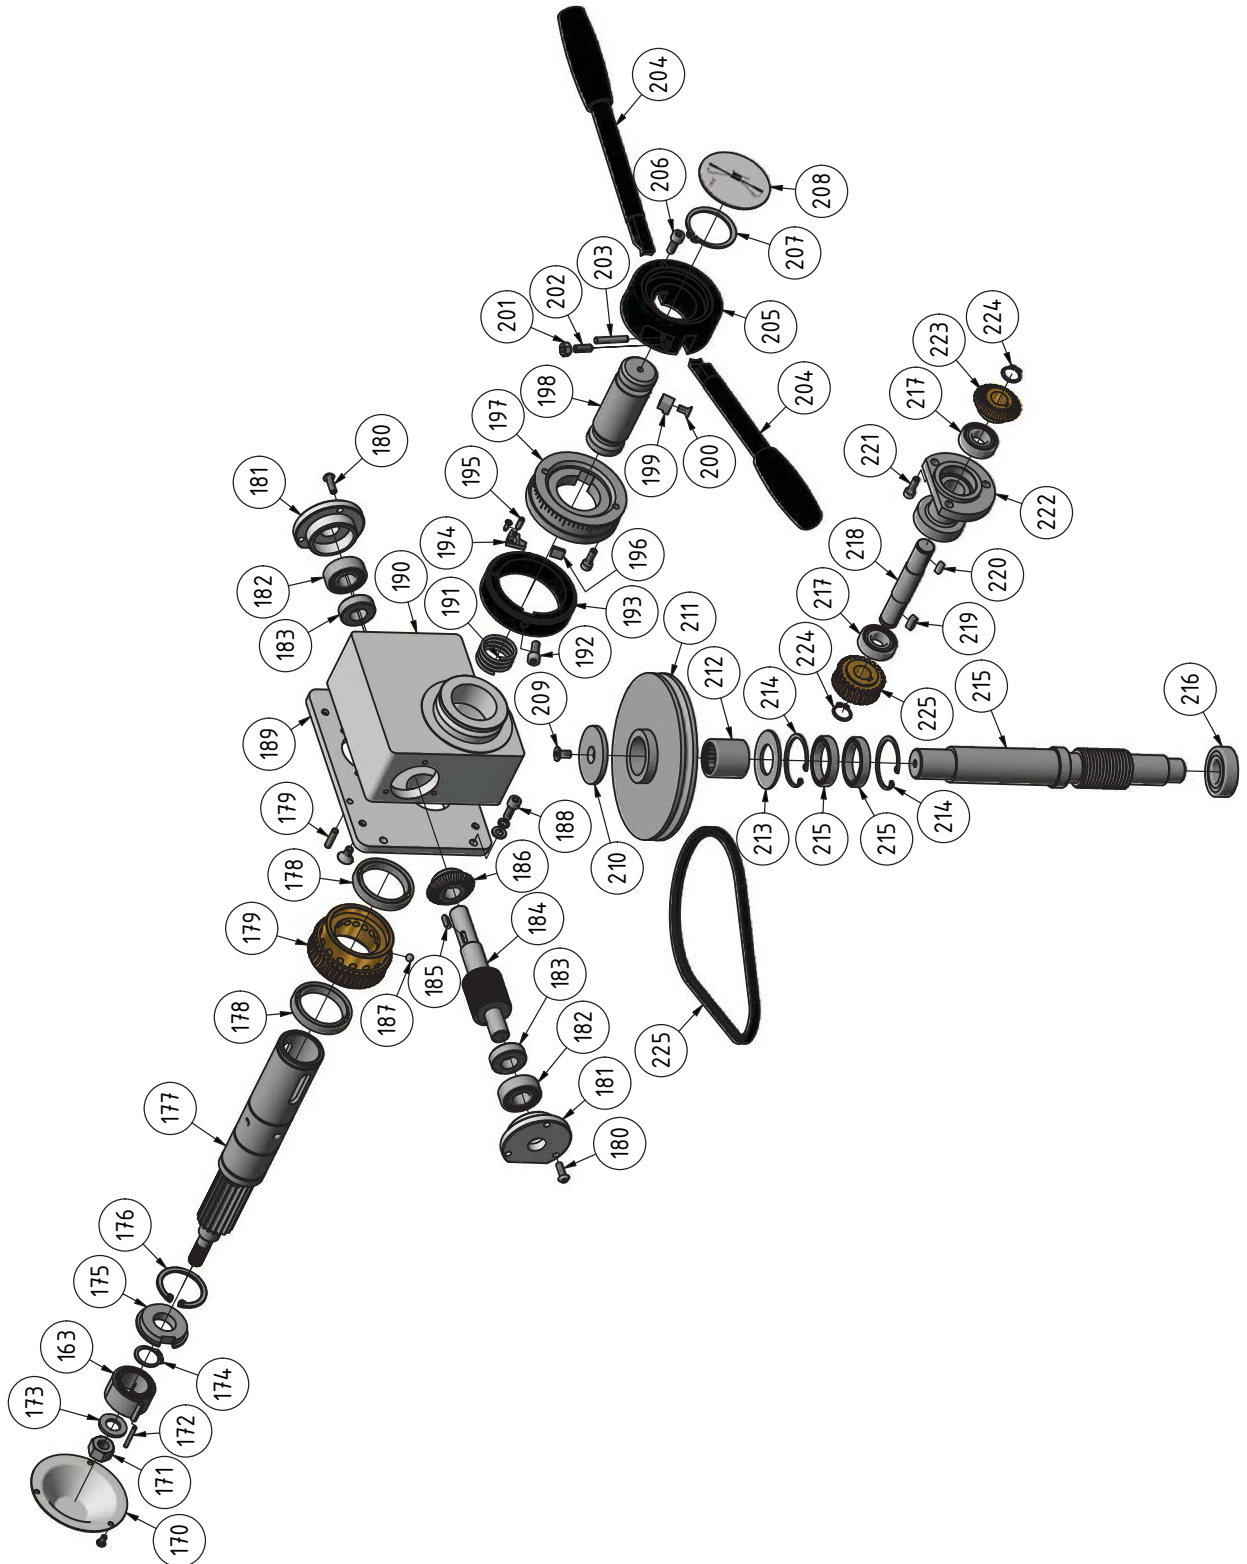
Pinolenvorschub - Spindle sleeve feed
